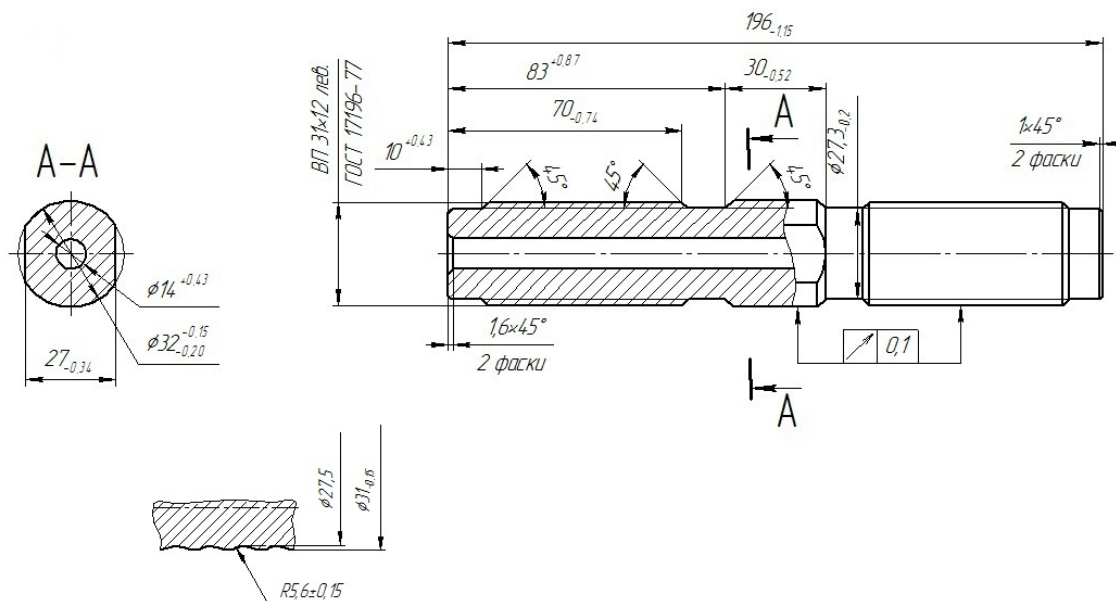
Ниппельное соединение закрытого типа бурильных труб
